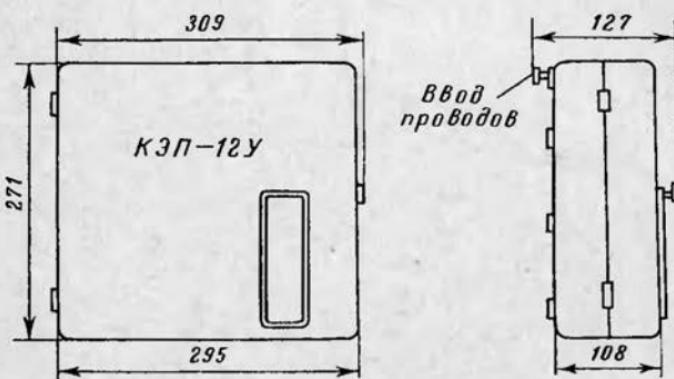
Конструкция командного электропневматического прибора типа КЭП-12У.
